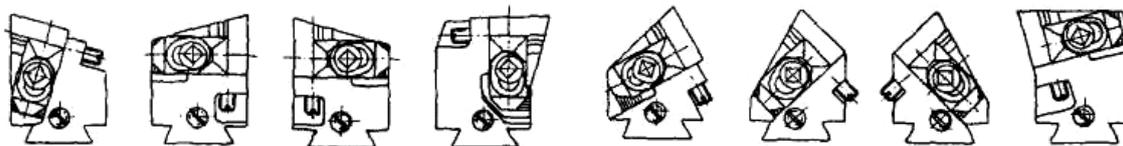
Резцовые блоки с креплением режущих пластин без отверстия
